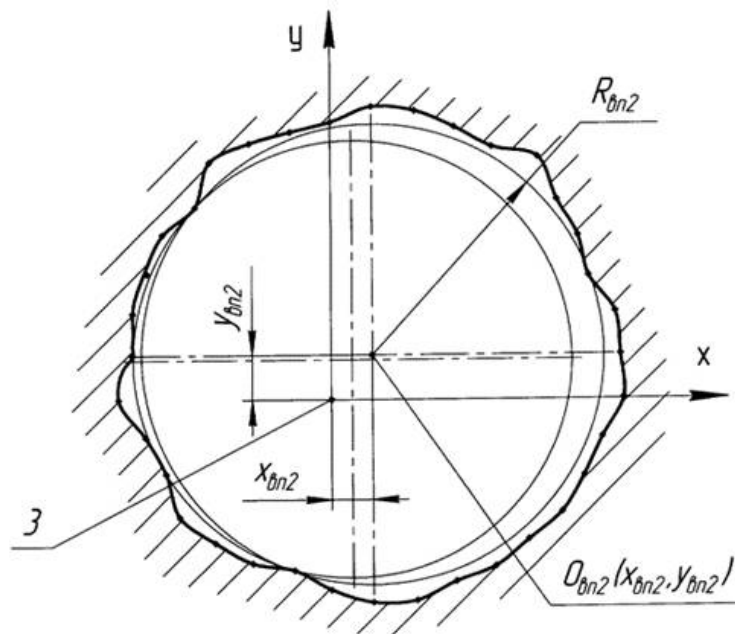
Схема визначення вписаного кола перетину базової поверхні деталі
